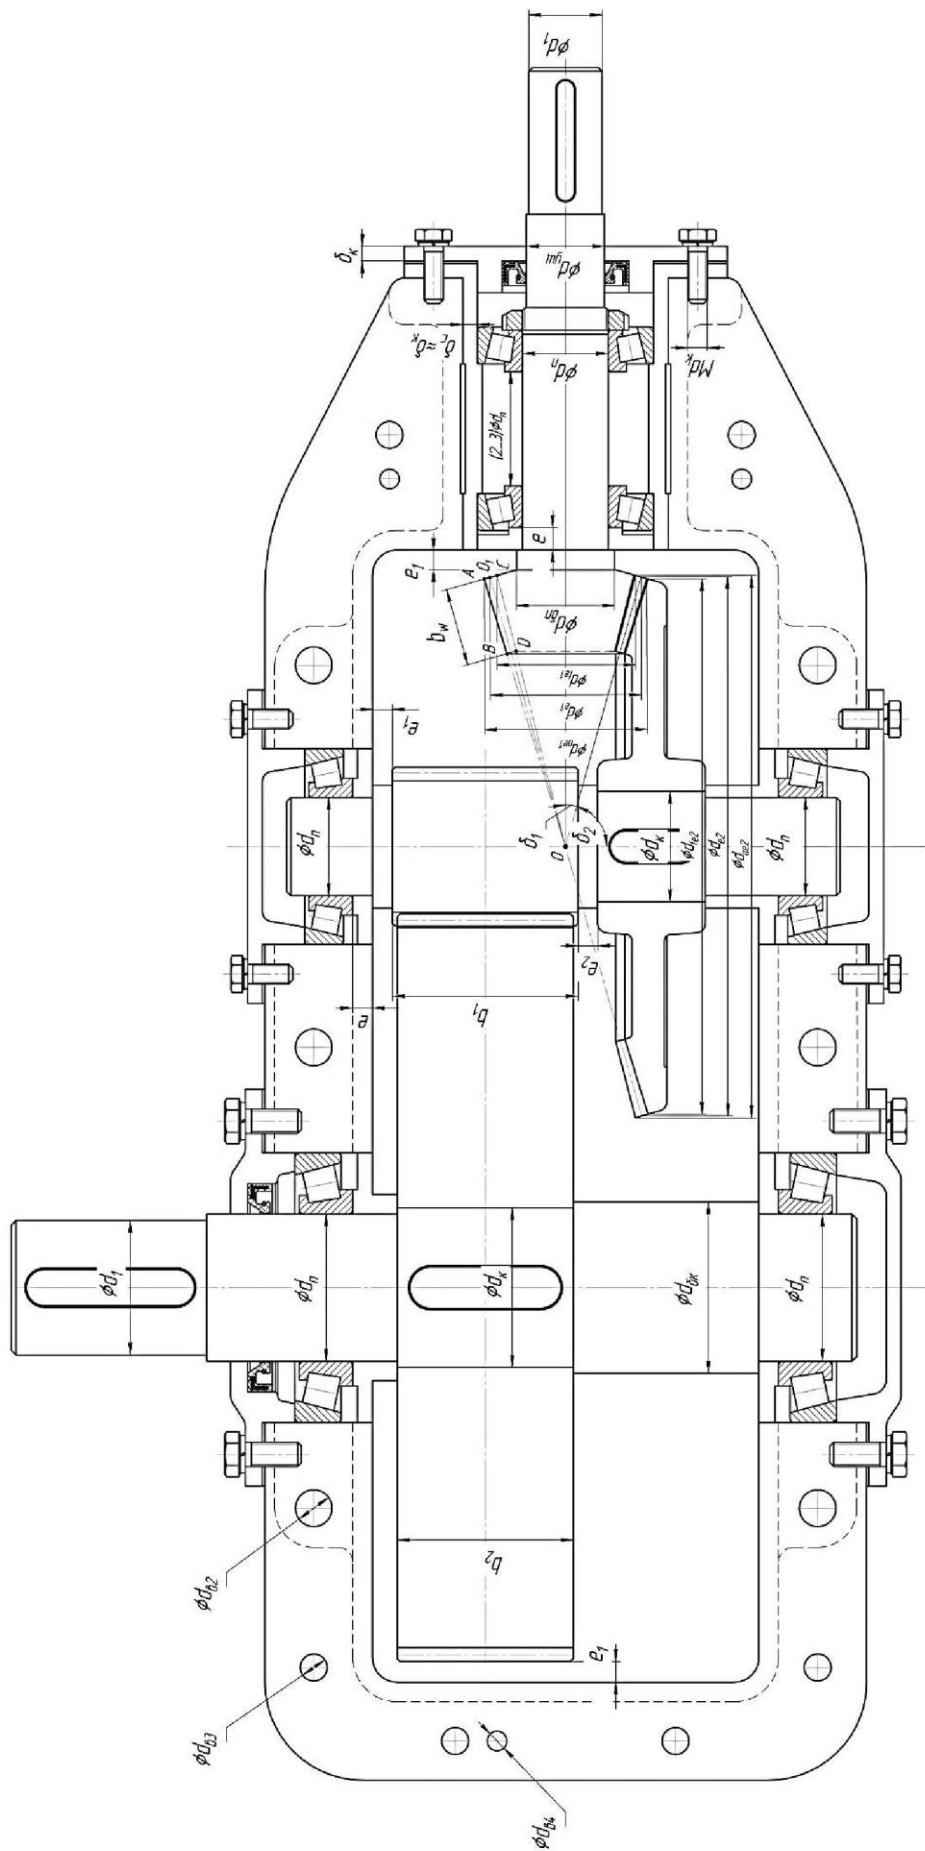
Компонувальне креслення конічно-циліндричного редуктора (закінчення)
